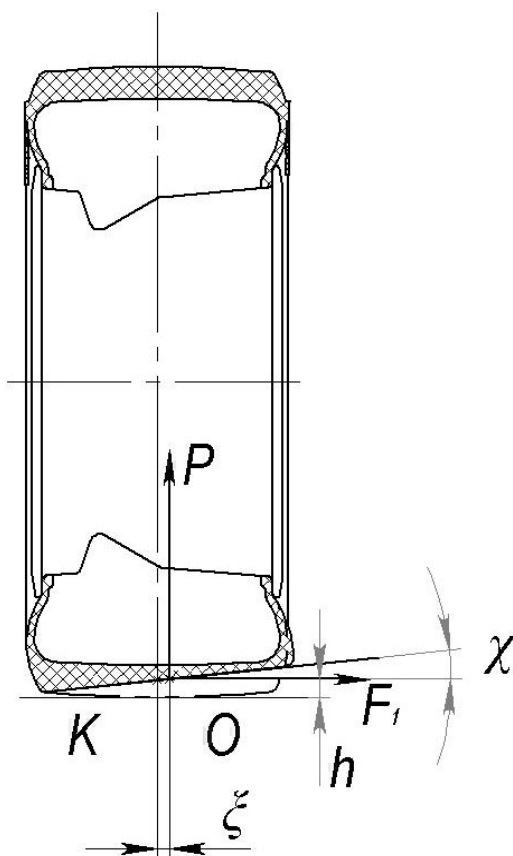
Розрахункова схема з рухливою опорною поверхнею
